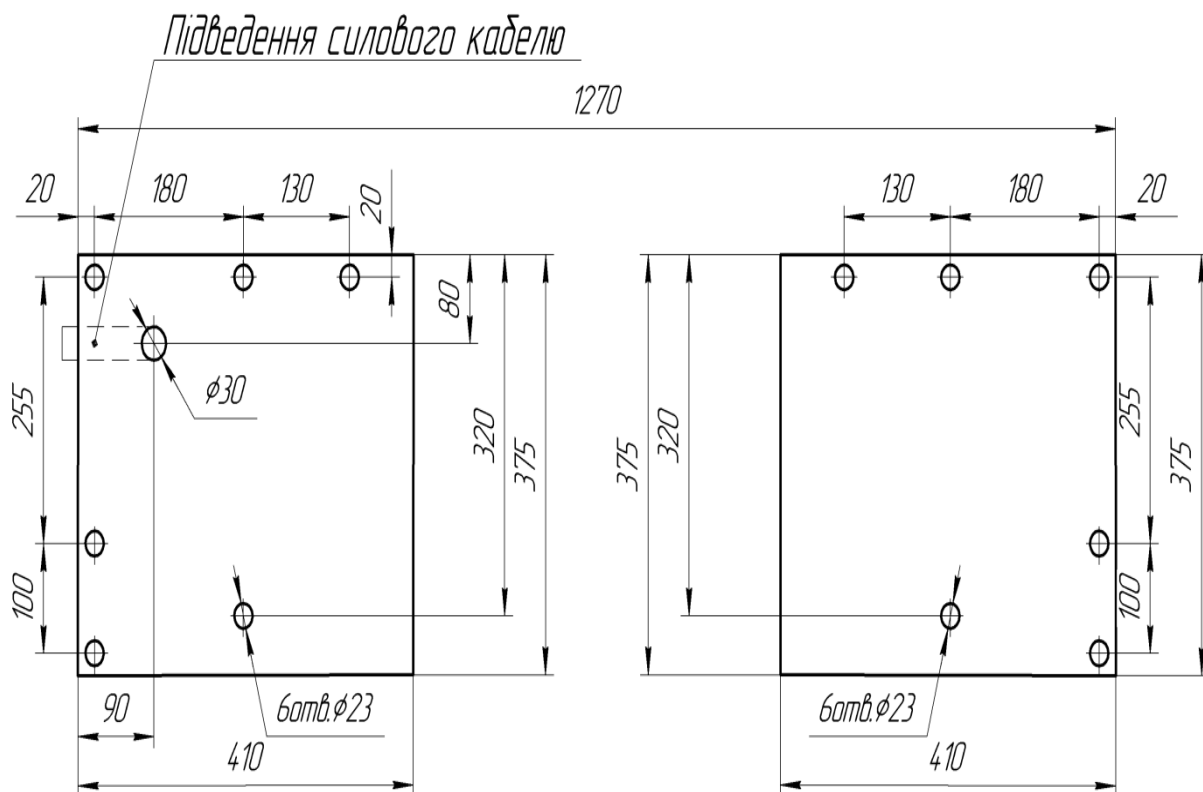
Установочний кресленик гальмівного стенда
